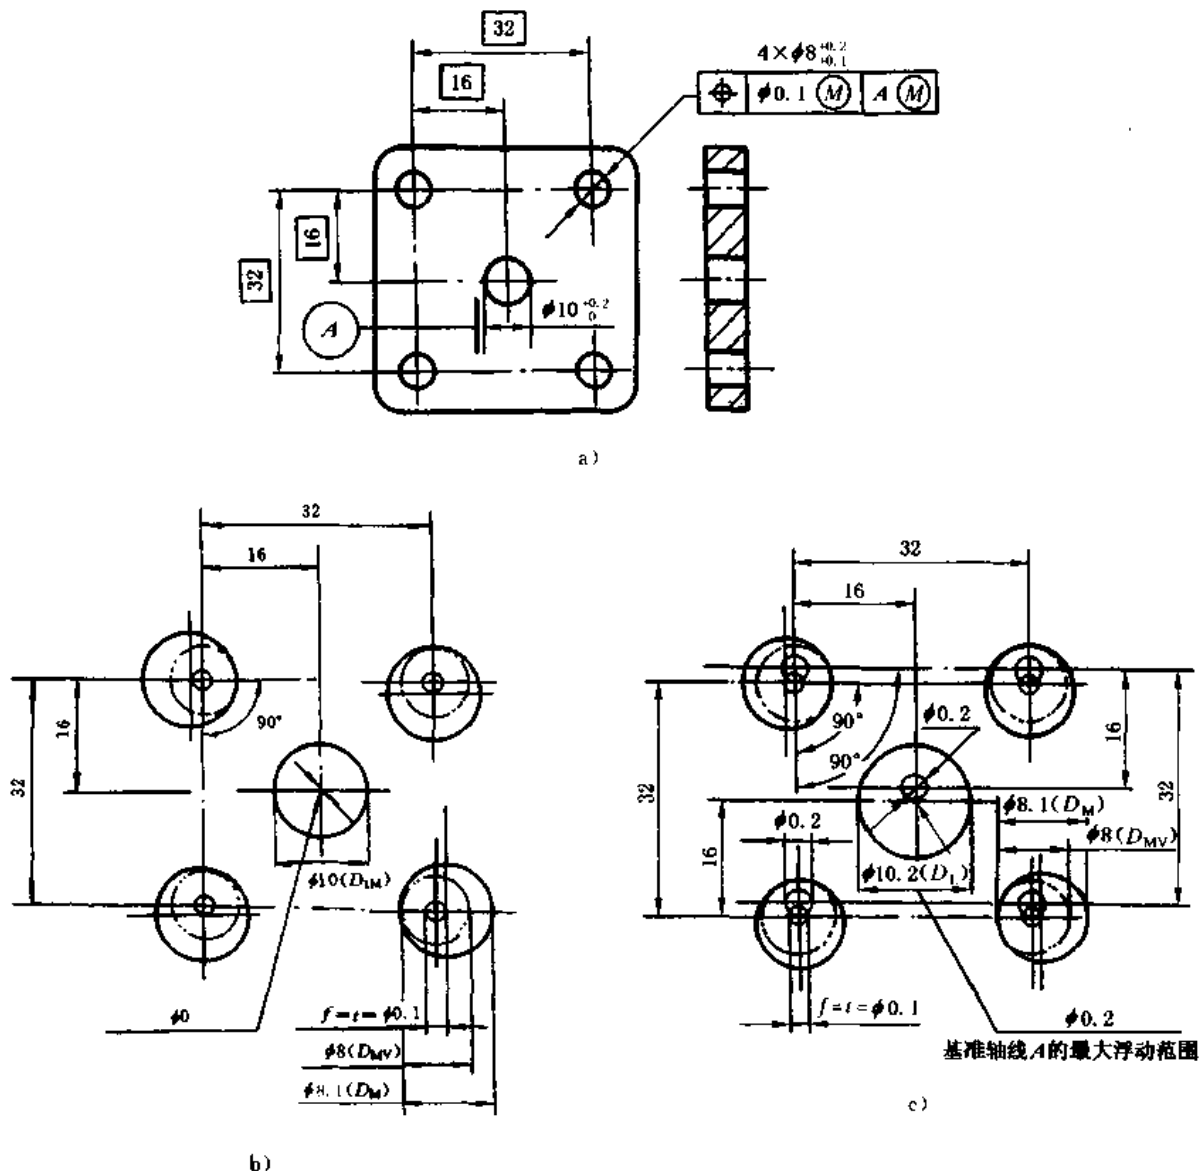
最大实体要求应用于成组要素位置度公差和基准要素
